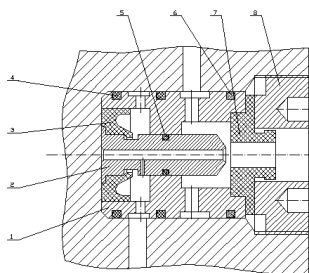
Клапан барабана. 1-корпус клапана; 2-поршень; 3-накладка; 4,6-ущільнюючі кільця; 7-сідло; 8-гайка
